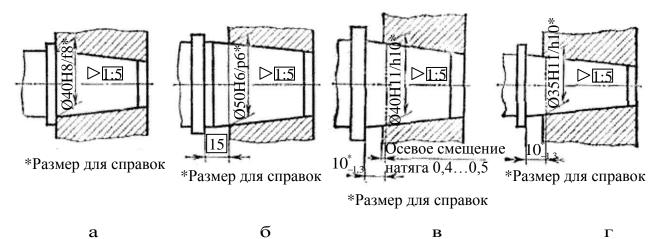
Варианты обозначения размеров и посадок на чертежах конических соединений
